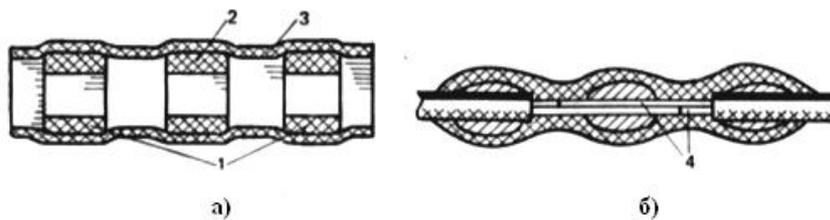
Схема соединения ленточных проводов: а) термоусадочной паяльной муфтой; б) загерметизированное соединение.
